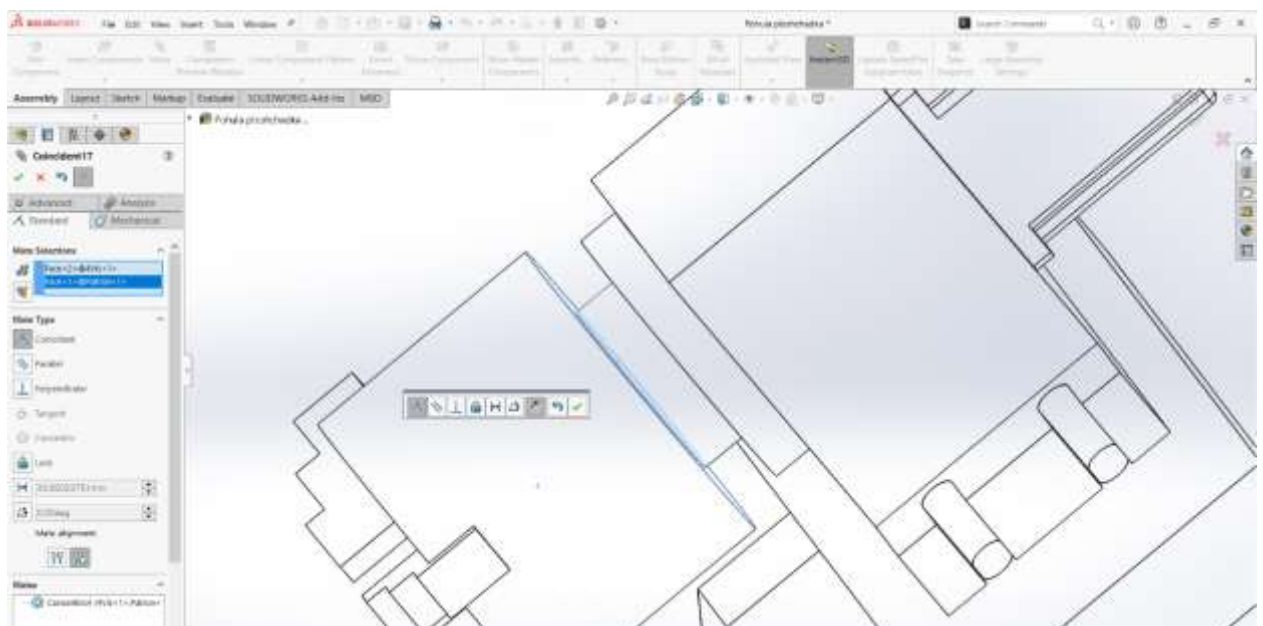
З'єднання патрона з поворотним механізмом
